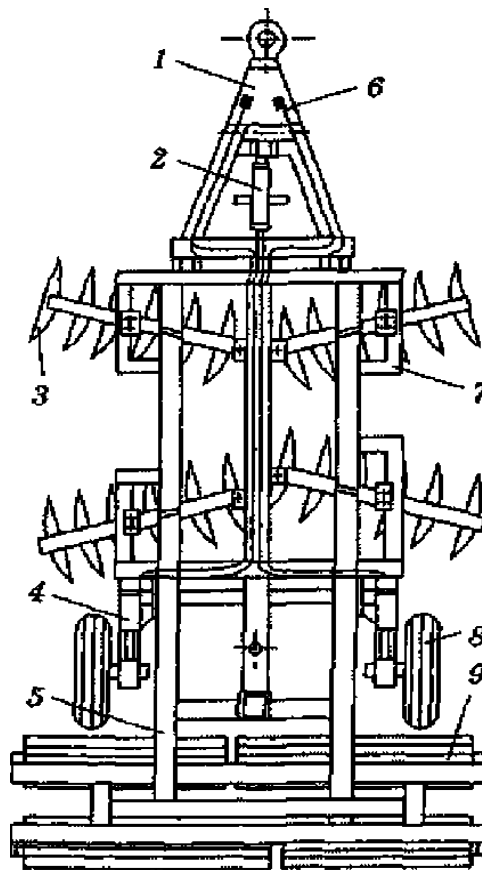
Борона дискова важка БДВ-3М: 1 - причіпний пристрій; 2 - вузол регулювальний; 3 – робочі органи (диски); 4 – вісь підймальна; 5 - рама; 6 – елементи гідросистеми; 7 - вузол регулювальний кута атаки робочих органів; 8 - колесо; 9 - прутковий каток дворядovий.
